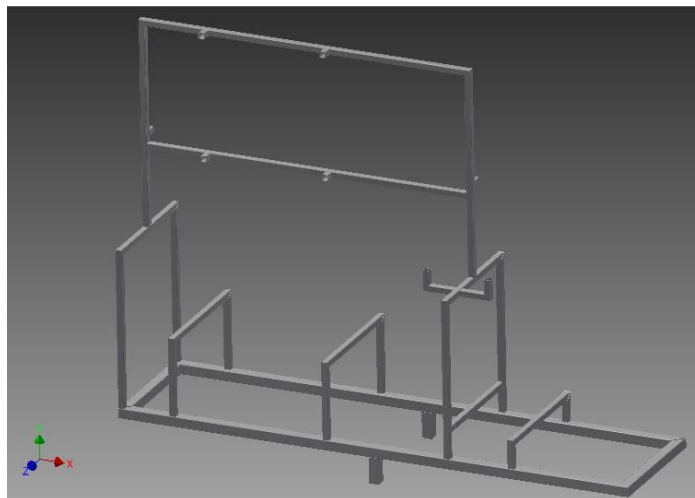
Estructura soporte en tubería cuadrada de acero inoxidable. Fuente: Autor
